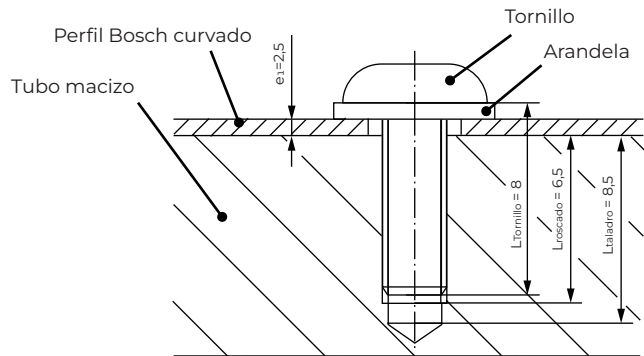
Unión 1 - Planteamiento inicial del montaje
